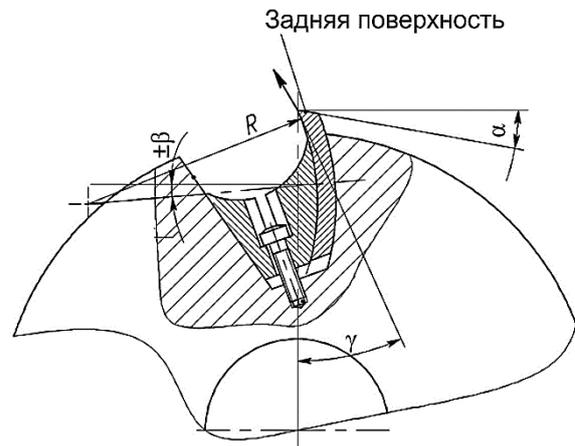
Узел крепления фрезы с радиусными режущими пластинами и его геометрические параметры
